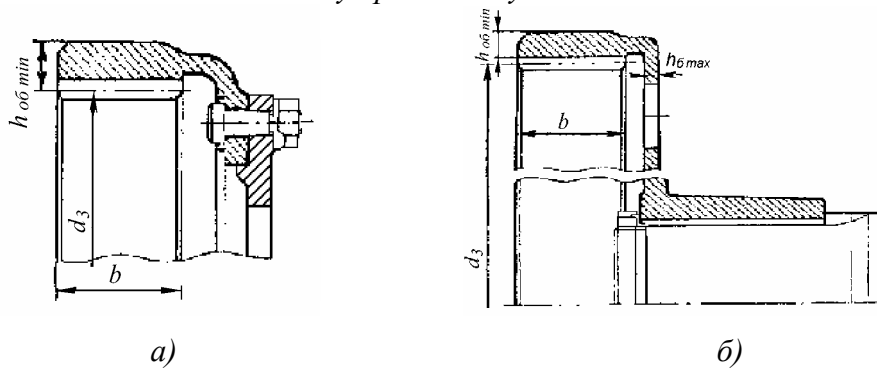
Неплавающие вращающиеся центральные колеса с внутренними зубьями
